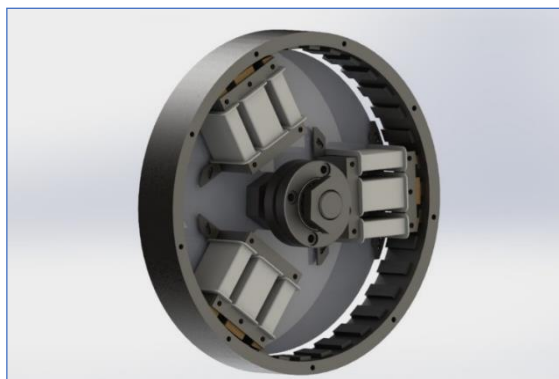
Вид в сборе универсального генератор-двигателя Баялиева
